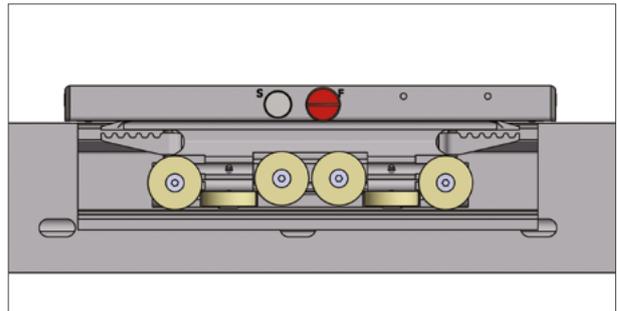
SNR – Linearachse mit Polymer – Laufrollenführung
